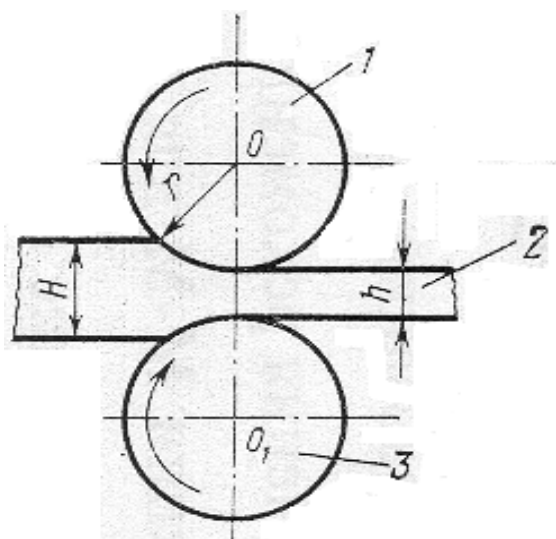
Схема продольної прокатки: 1 – верхній валок; 2 –штаба; 3 – нижній валок.
